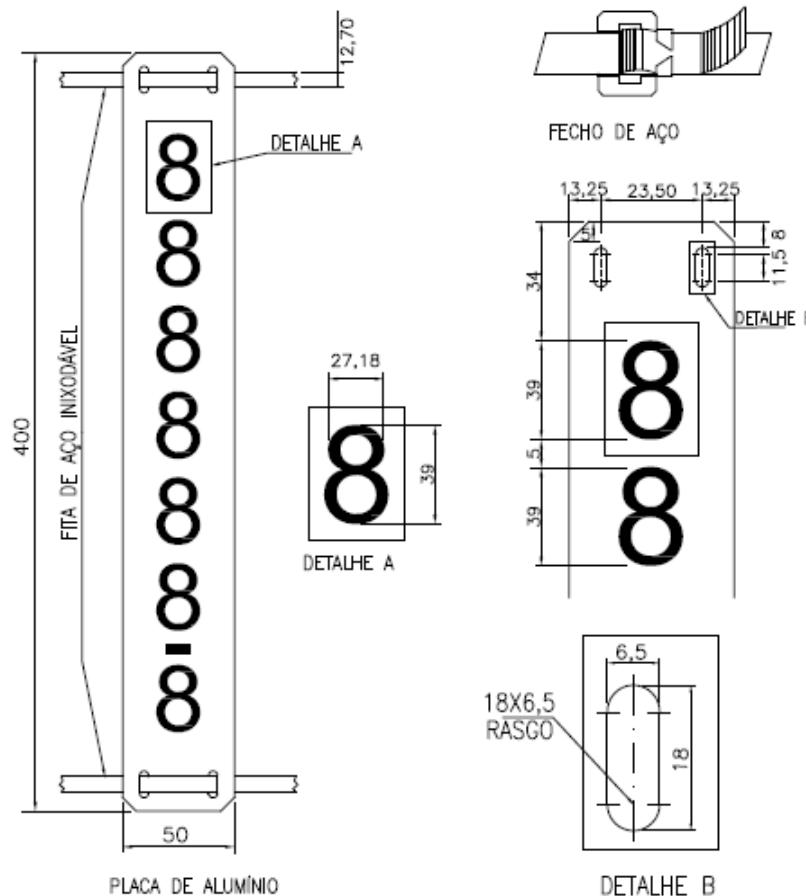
Placa de identificação de componentes. Chaves e equipamentos
